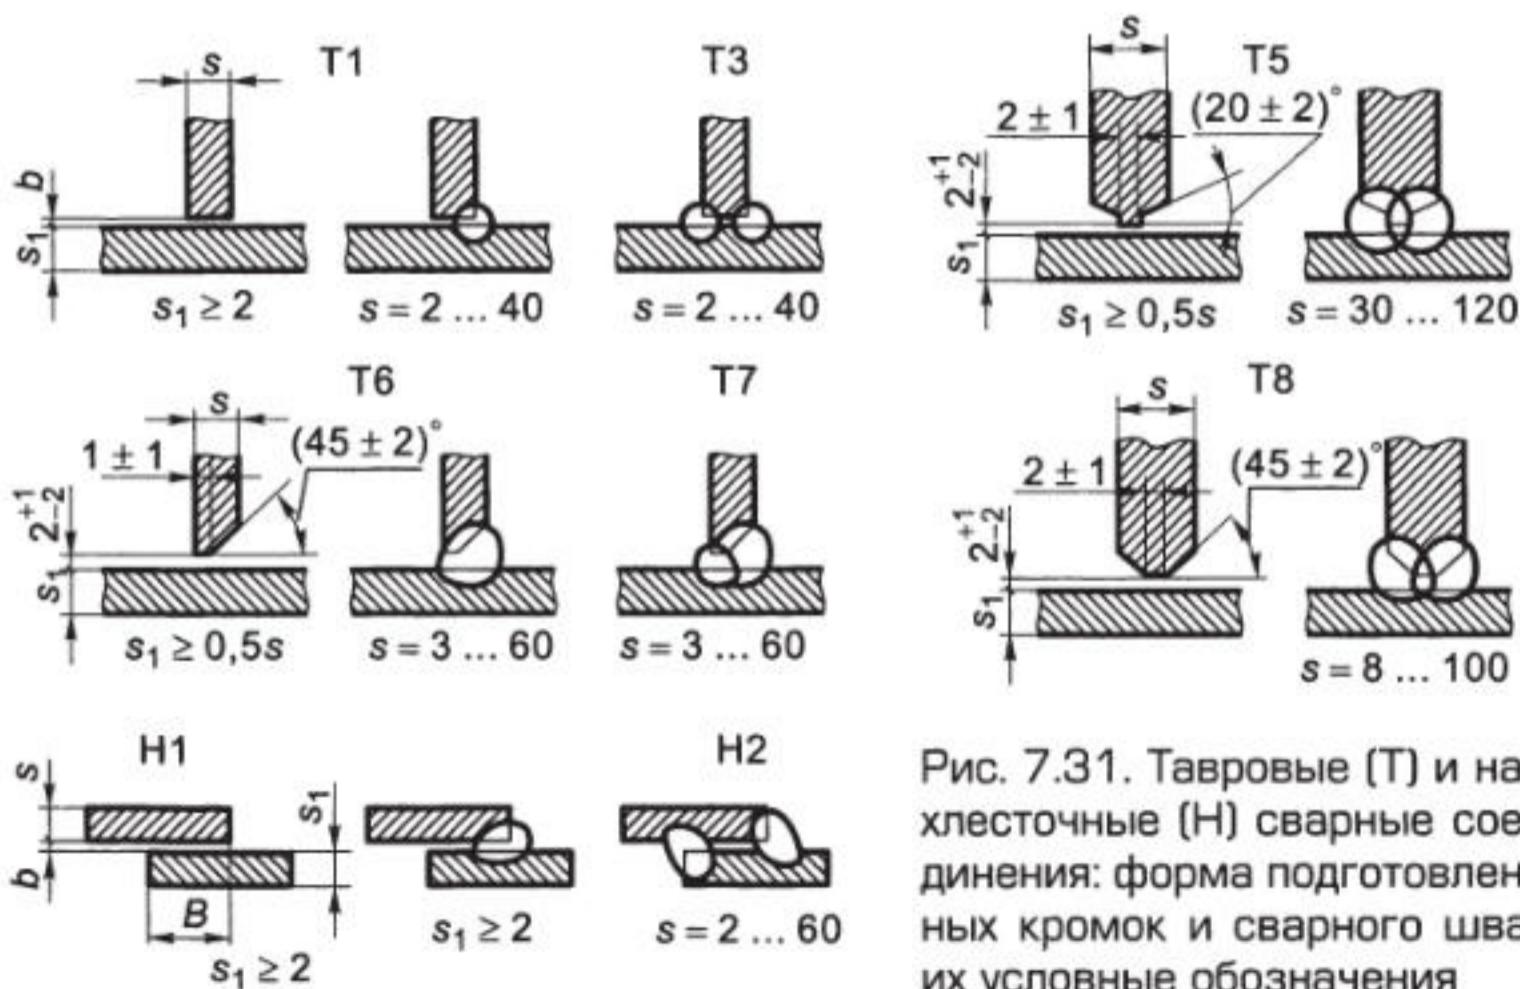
Тавровые (Т) и нахлесточные (Н) сварные соединения: форма подготовленных кромок и сварного шва, их условные обозначения
